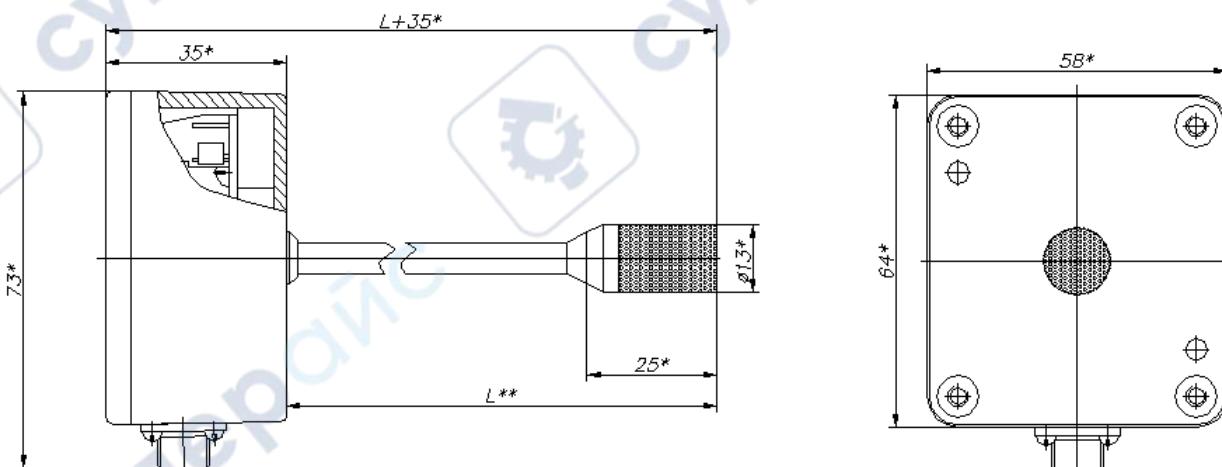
Измерительный преобразователь ИПВТ-03-14
